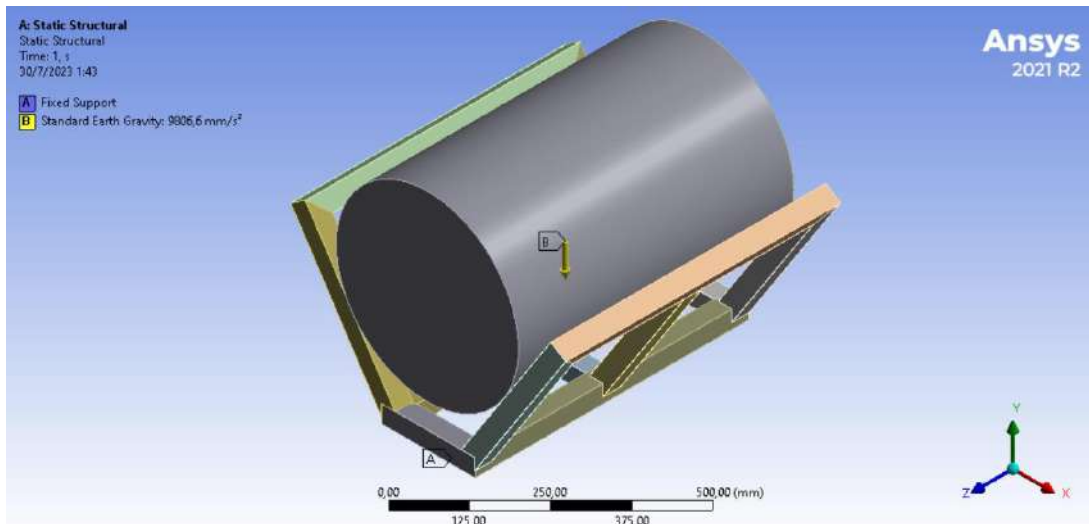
Fuerzas y apoyos aplicados en la estructura móvil.
